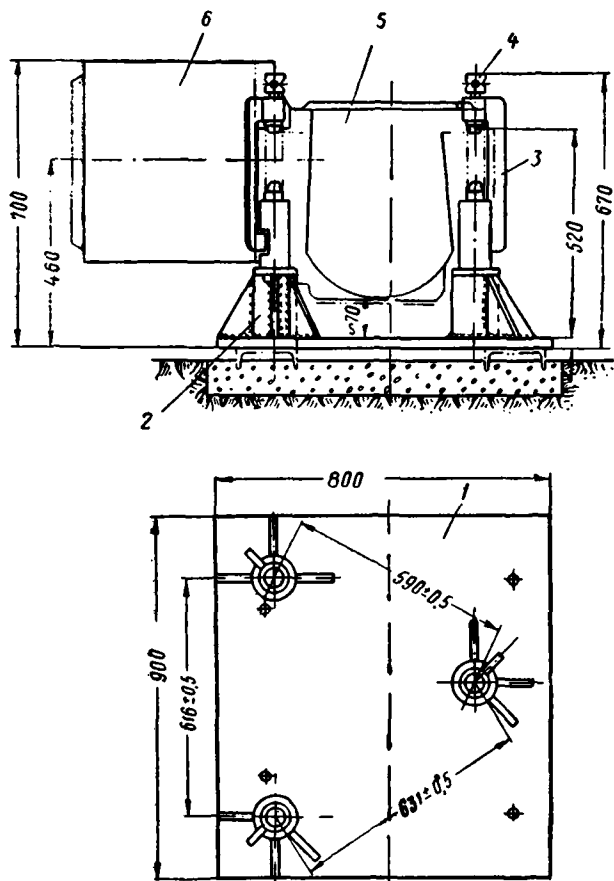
Приспособление для сборки двигателя ДК-406 с компрессором Э-400
